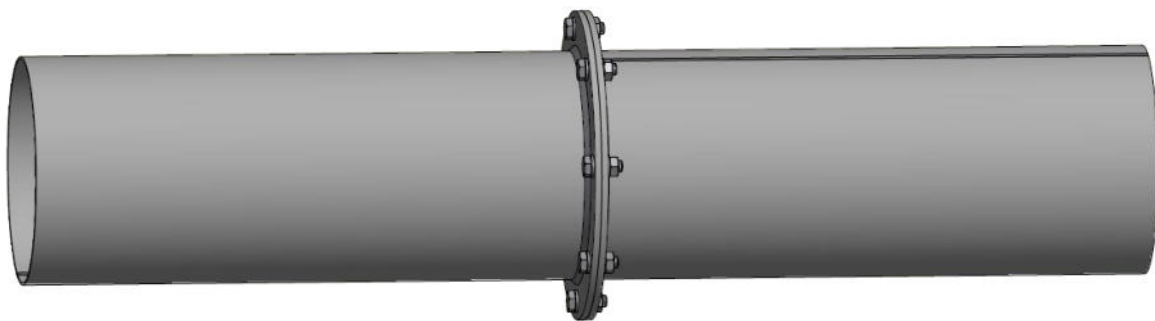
Montierte Rohrleitung mit Flanschen.
